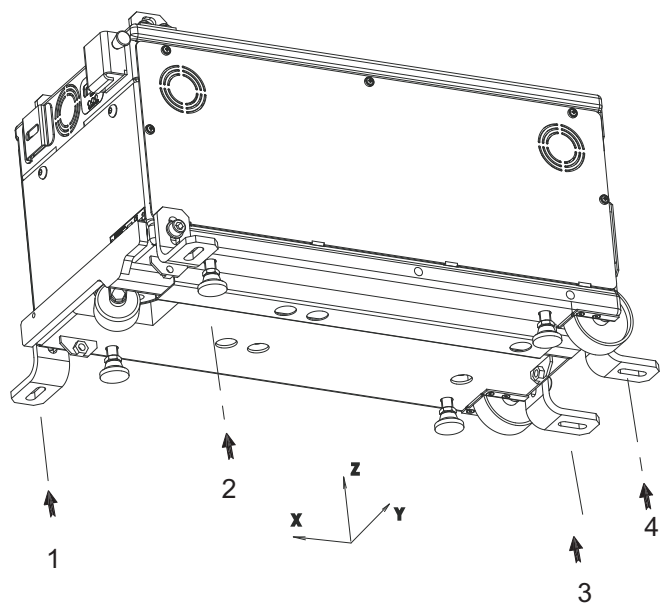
Dimensions de la pompe équipée d'équerres parasismiques
